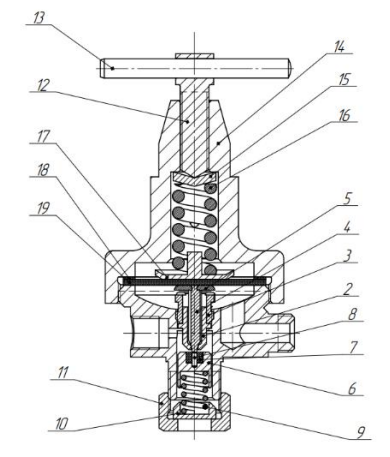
Схематическое изображение кислородного редуктора [6]
